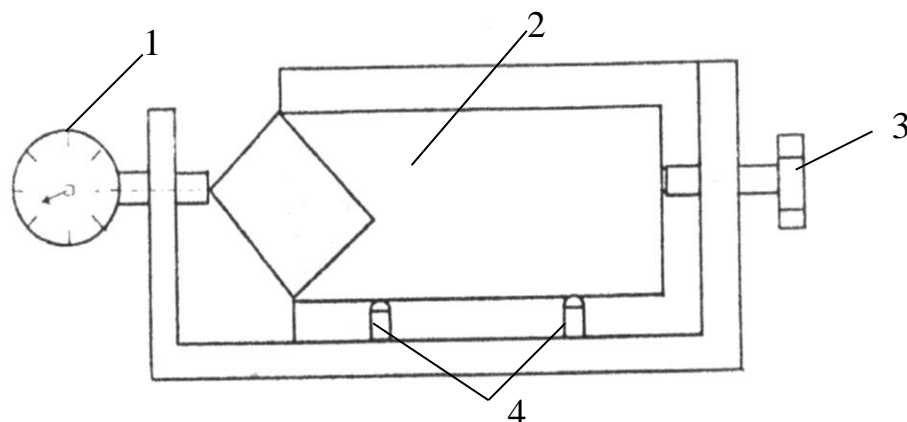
Пристосування для вимірювання розмірного зносу різців: 1 – індикатор; 2 – різець; 3 – упорний гвинт; 4 – опори
